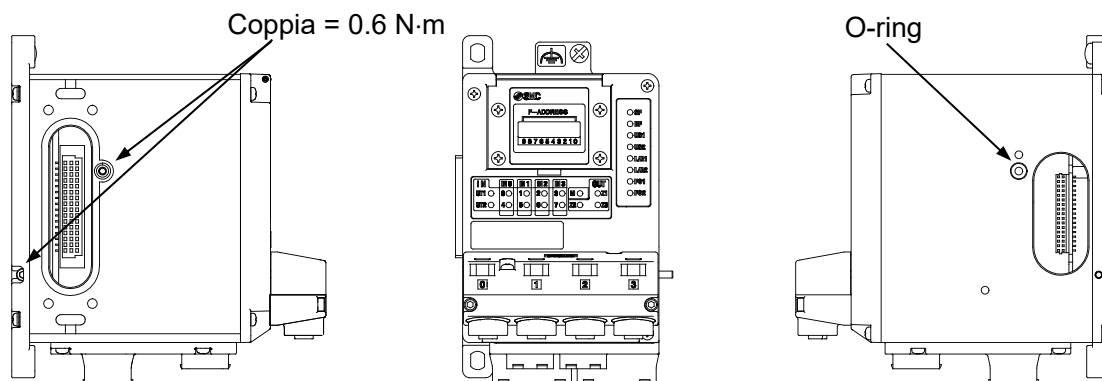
Collegamento per il manifold di elettrovalvole
